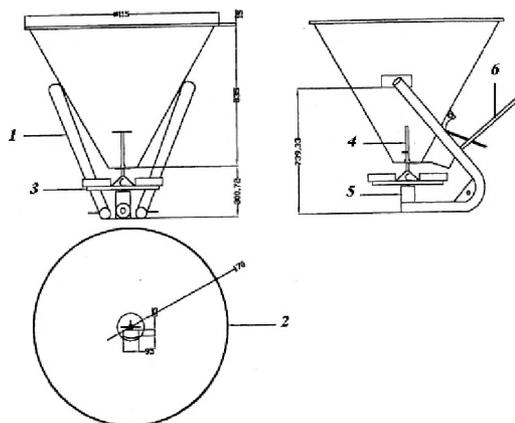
Схема навесного дискового разбрасывателя твердых минеральных удобрений (размеры указаны в миллиметрах): 1 — рама, 2 — бункер, 3 — диск-разбрасыватель с лопатками, 4 — туюнаправитель, 5 — система привода, 6 — рычаг регулировки подачи
